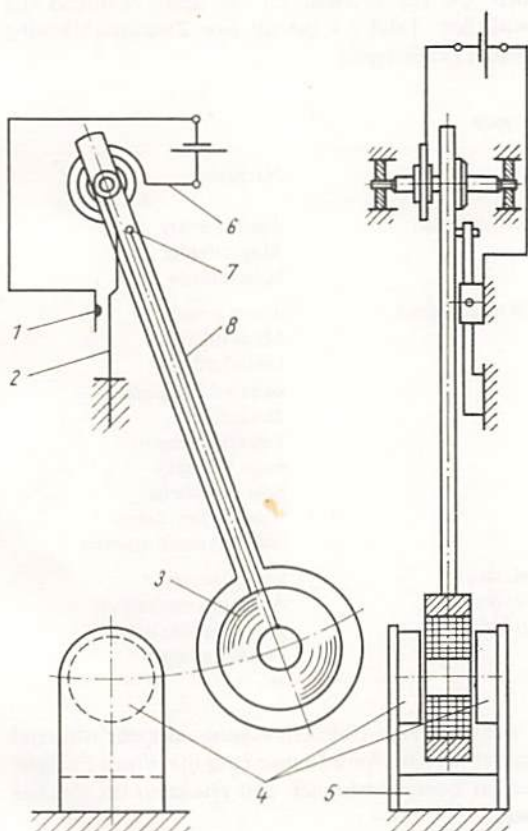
Kontaktgesteuertes Pendel mit schwingender Antriebsspule
